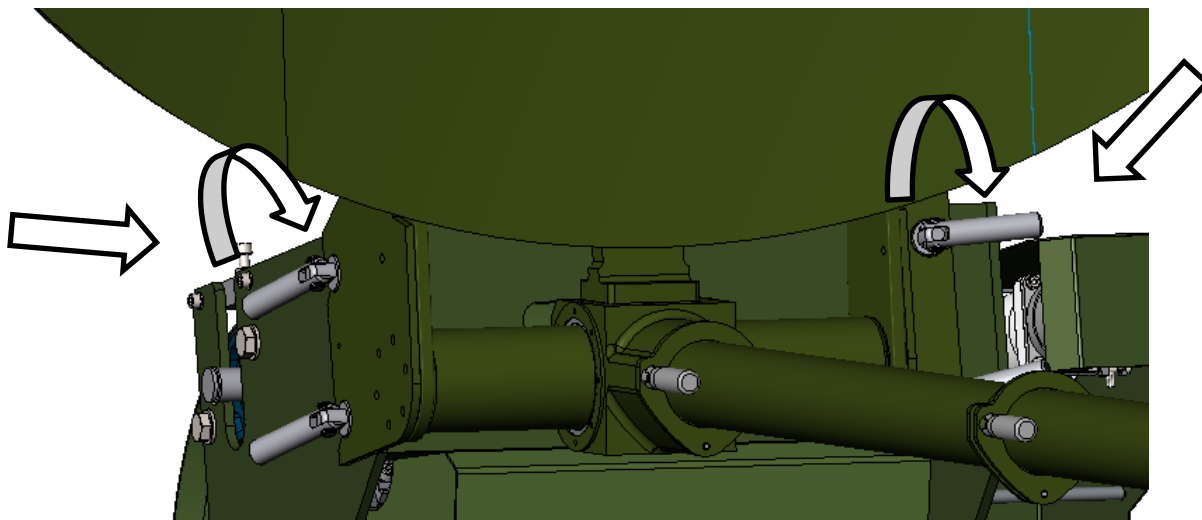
Стыковка лепестка рефлектора (№1)
